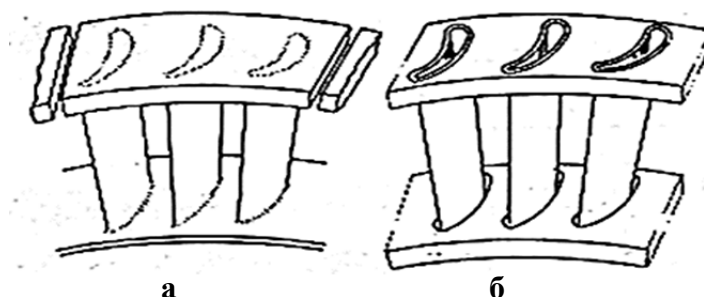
Жесткая конструкция направляющего аппарата (а) и допускающая свободное расширение лопаток (б) [4]
